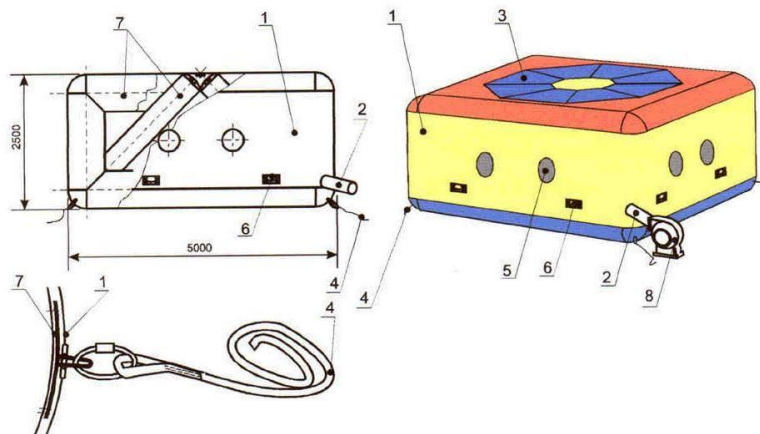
Устройство эвакуации Каскад-5. 1- тканевая оболочка; 2- рукав; 3- верхнее основание; 4- ленты (веревки); 5- окна; 6- ручки; 7- поддерживающий каркас; 8- вентилятор.
